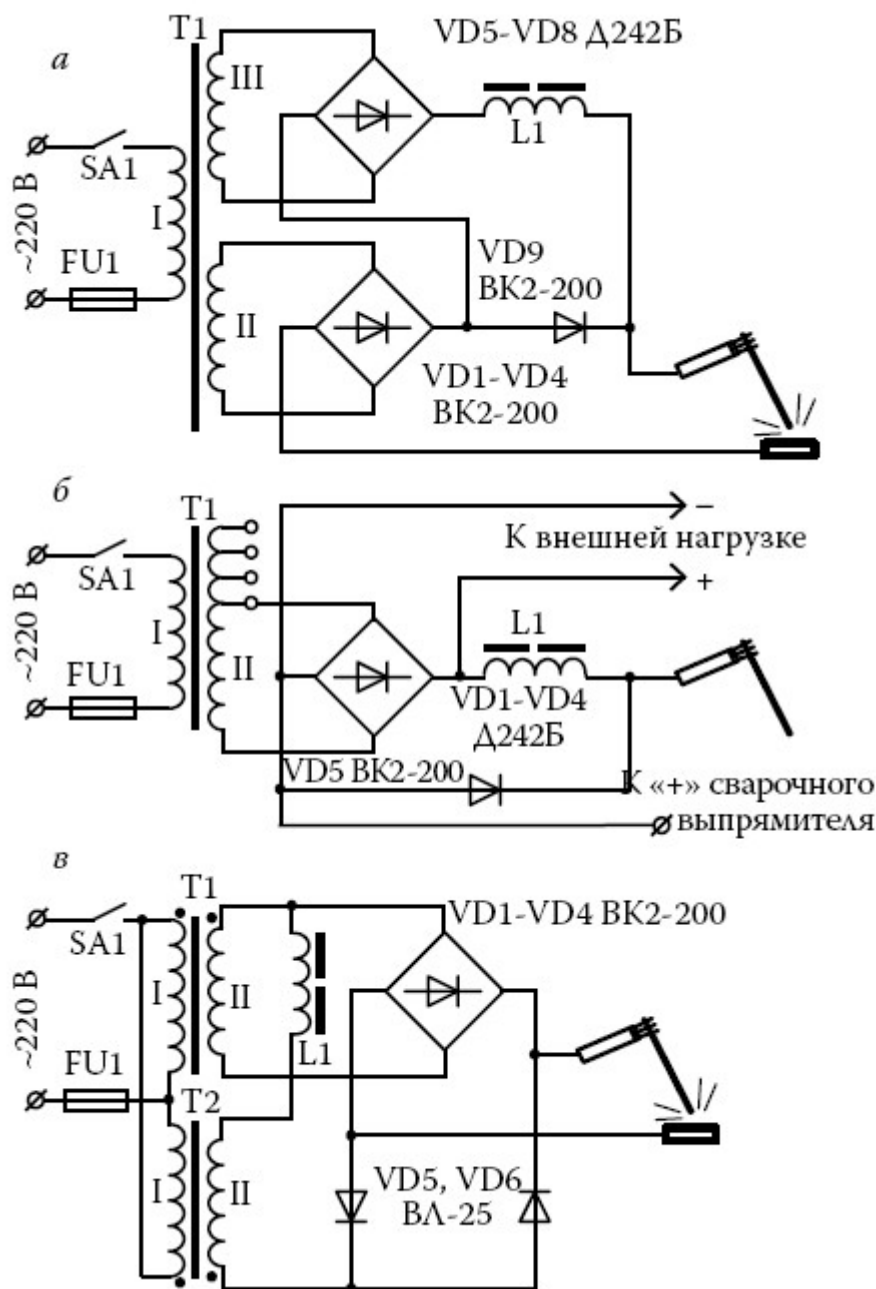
Схемы вольтдобавки для надежного зажигания сварочной дуги:
